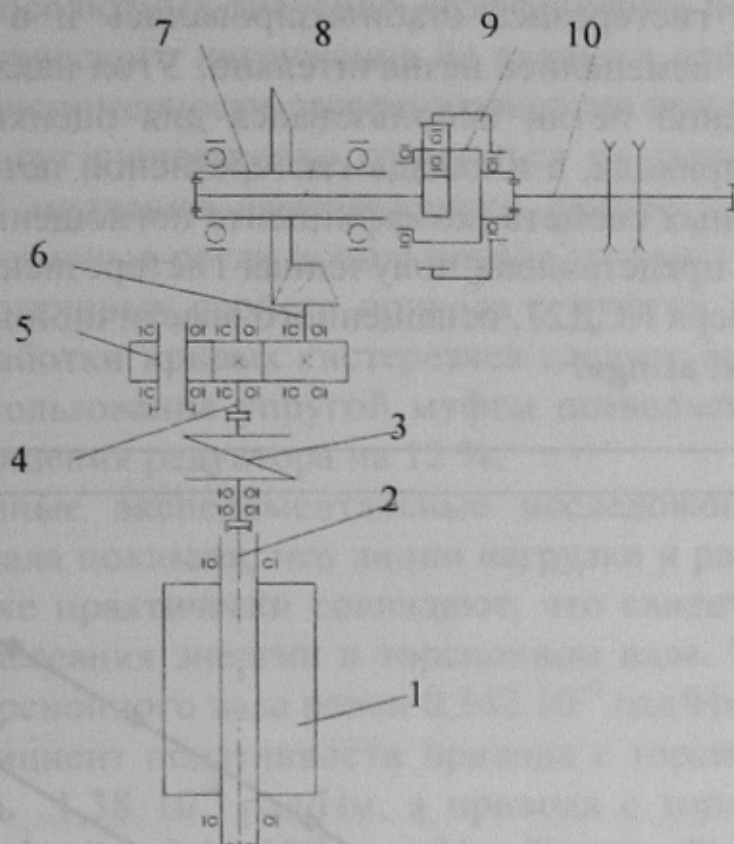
Кинематическая схема редуктора конвейера КСД27
